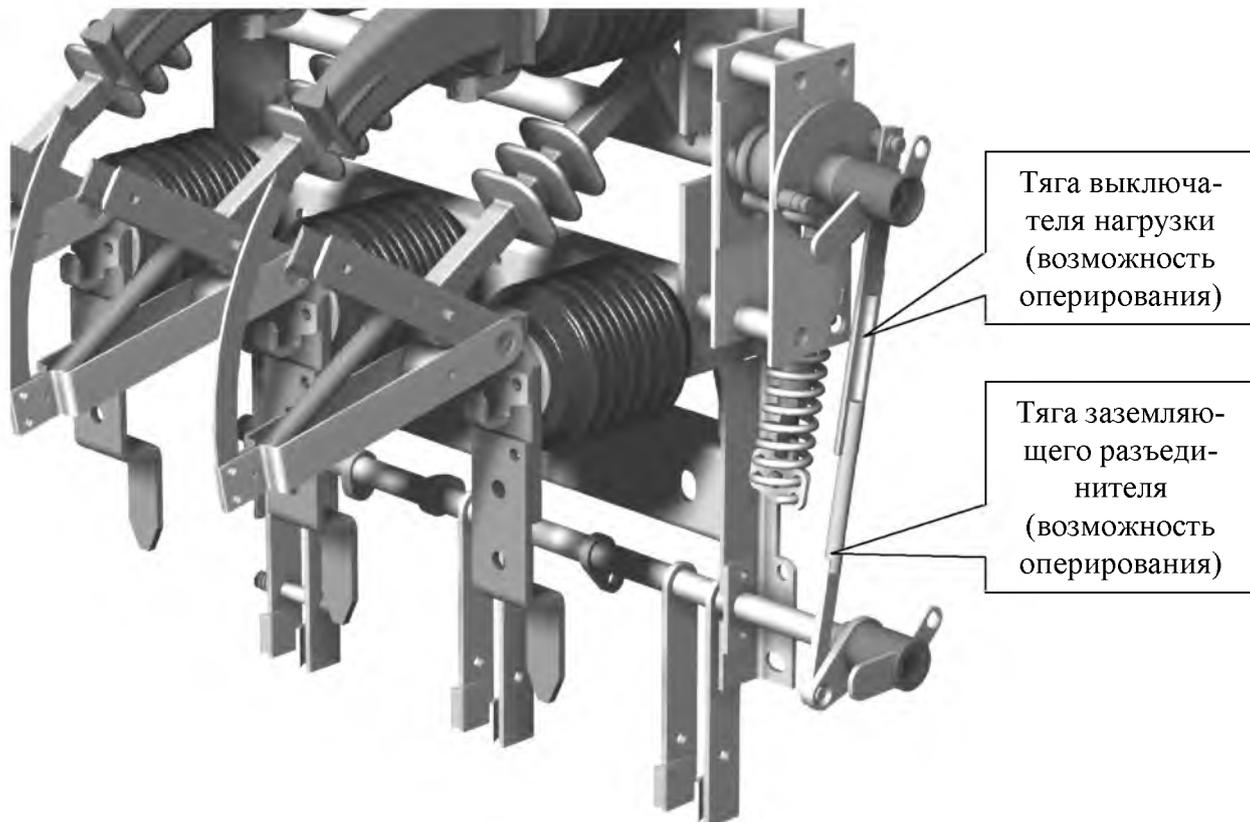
Блокировка выключателя нагрузки и заземляющего разъединителя (выключатель нагрузки отключен, заземляющий разъединитель отключен).
